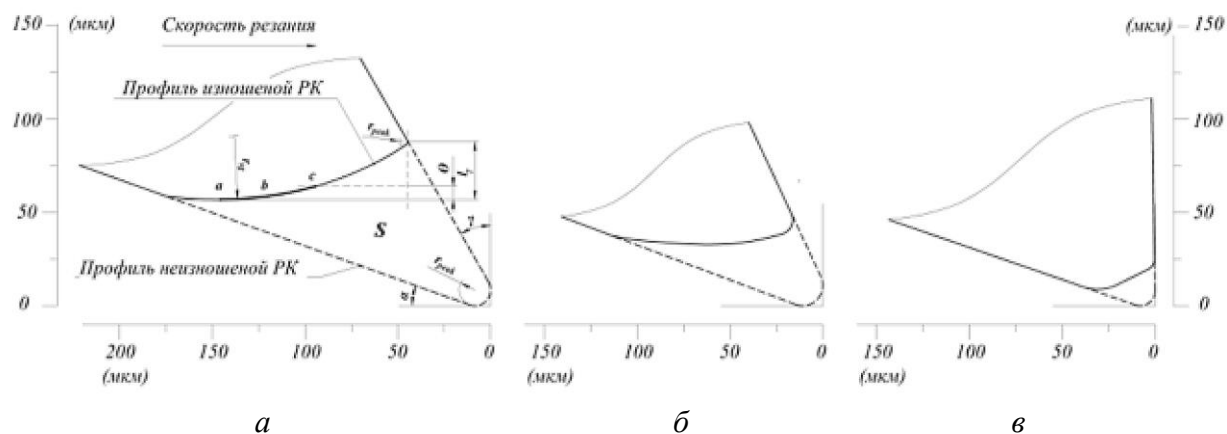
Профили режущих кромок сверл: а – из быстрорежущей стали; б – из твердого сплава; в – со вставками из АТП
